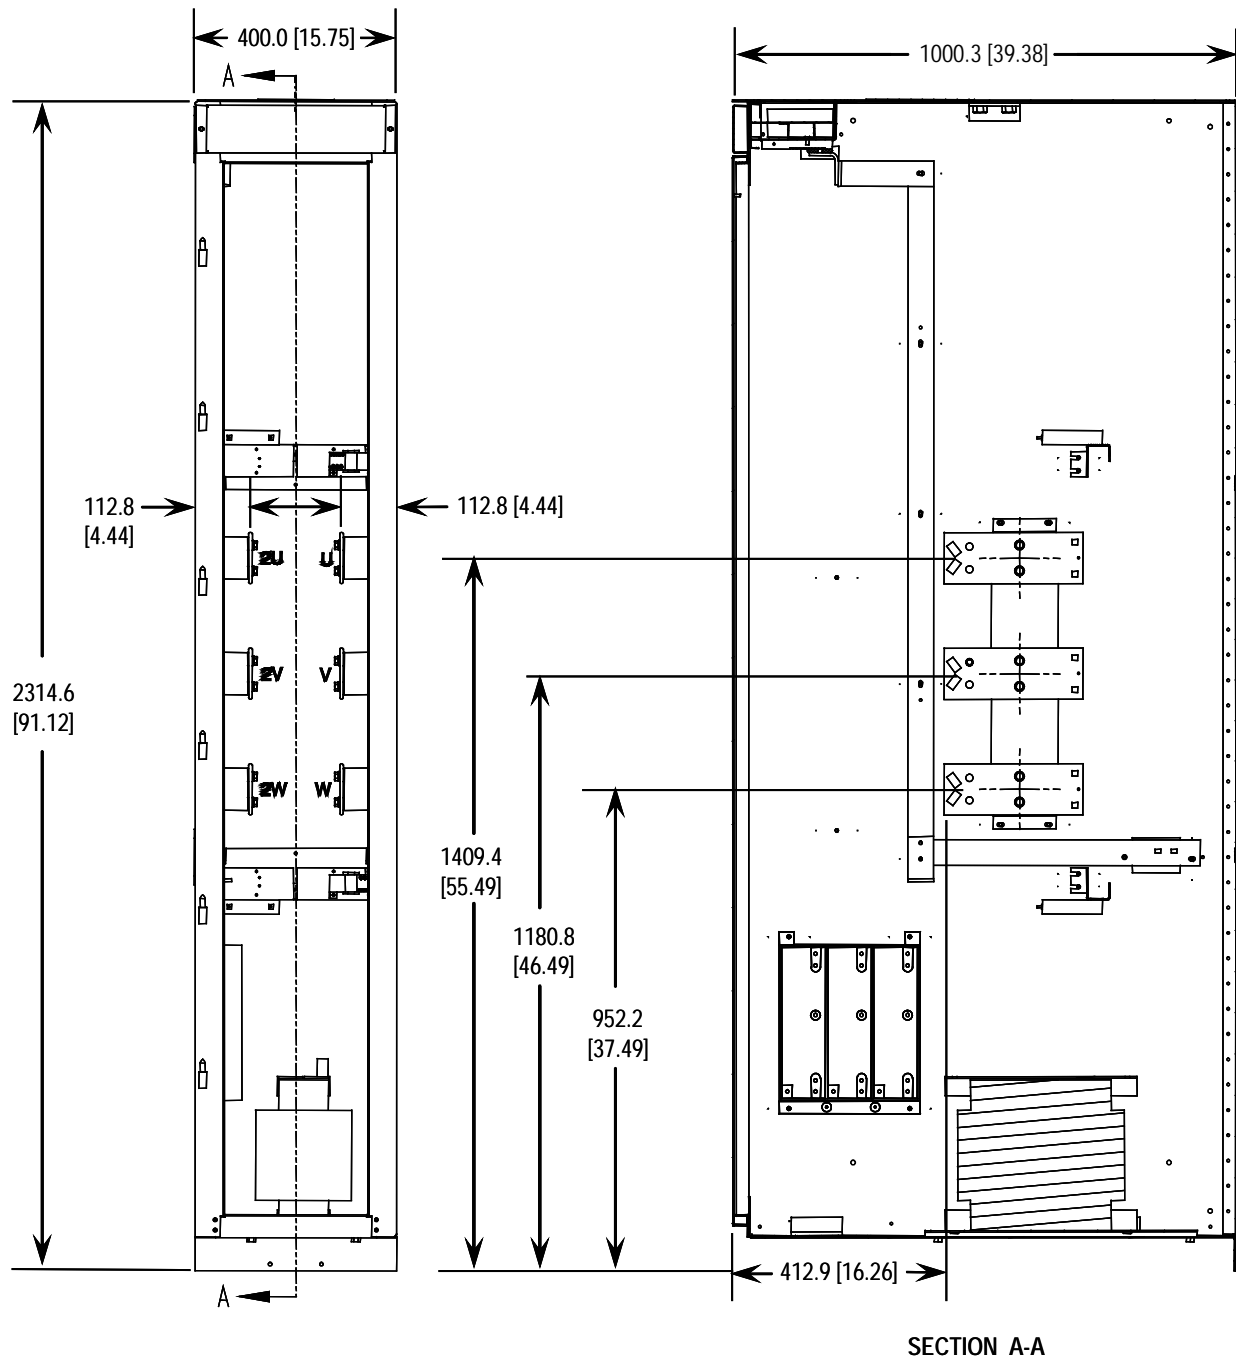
Viste dimensionali dell'armadio di cablaggio da 400 mm per la Configurazione 2 – morsetti motore lato linea e lato carico
